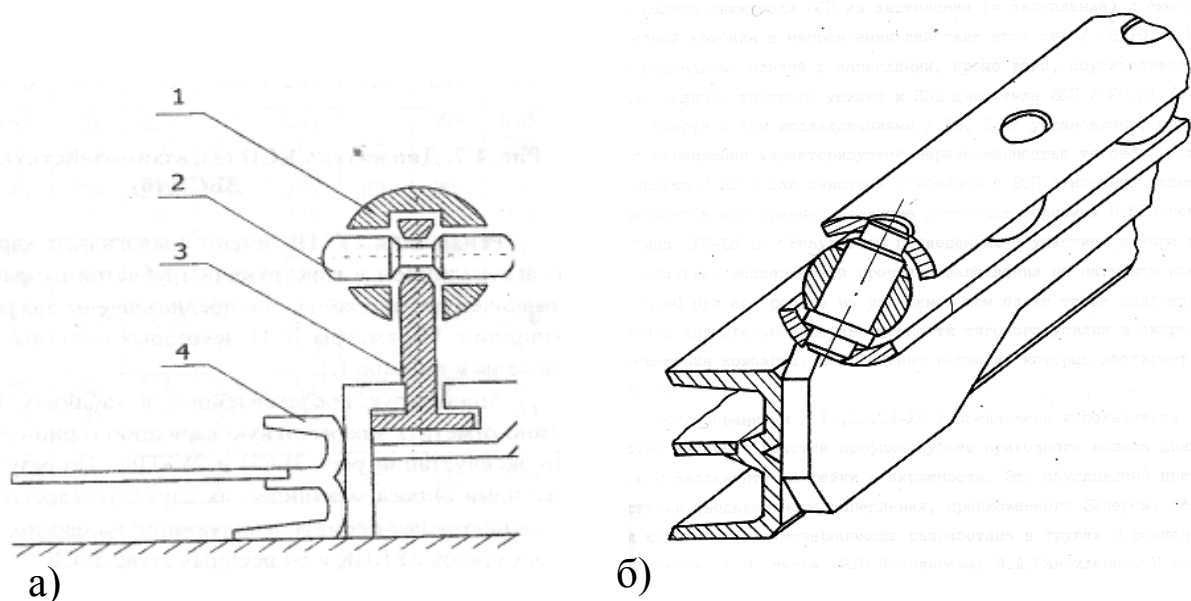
Рейка движителя БСП с сферическими цевками:
